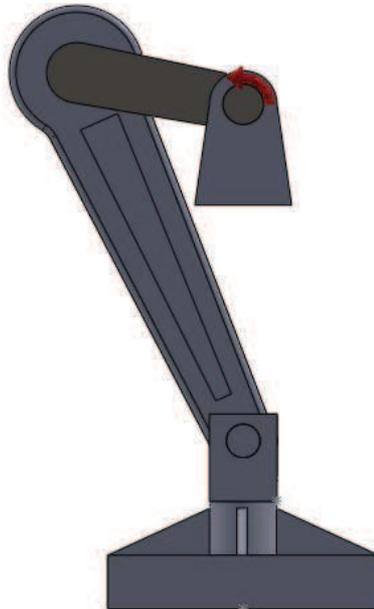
Representación de la posición del movimiento del motor del mecanismo de la compactadora.
